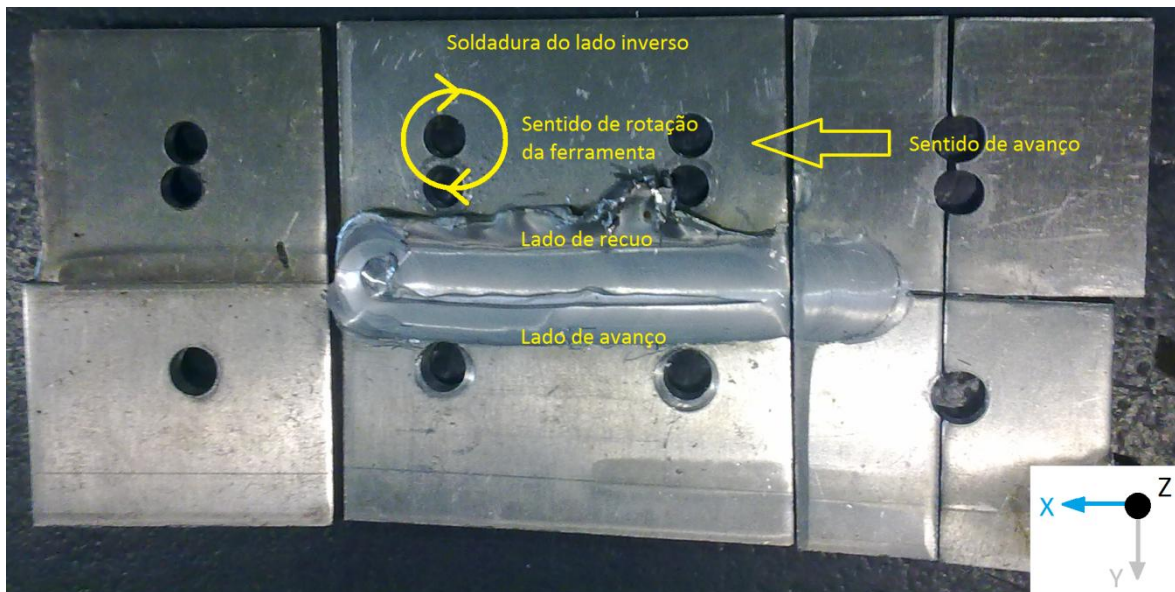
Parte inferior do provete soldado de ambos os lados
